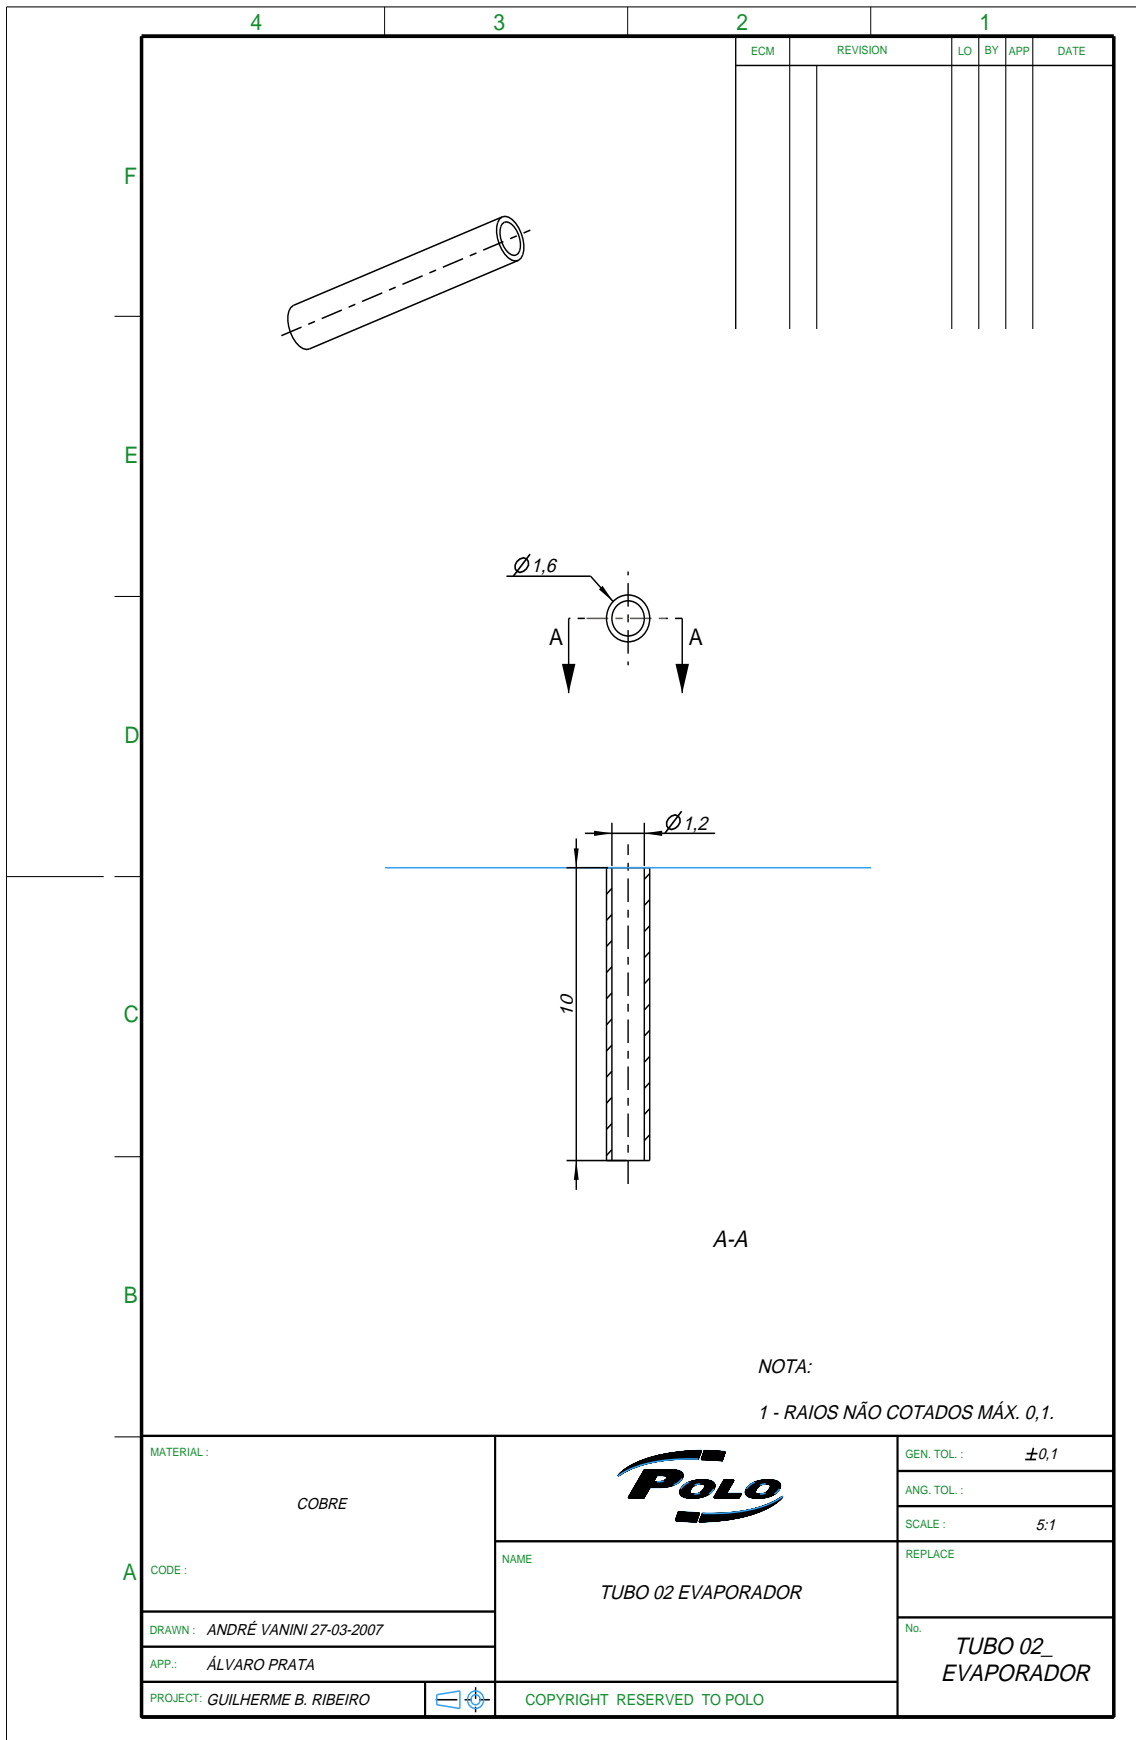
Desenho técnico do evaporador acoplado a tubos de calor - Parte VII
